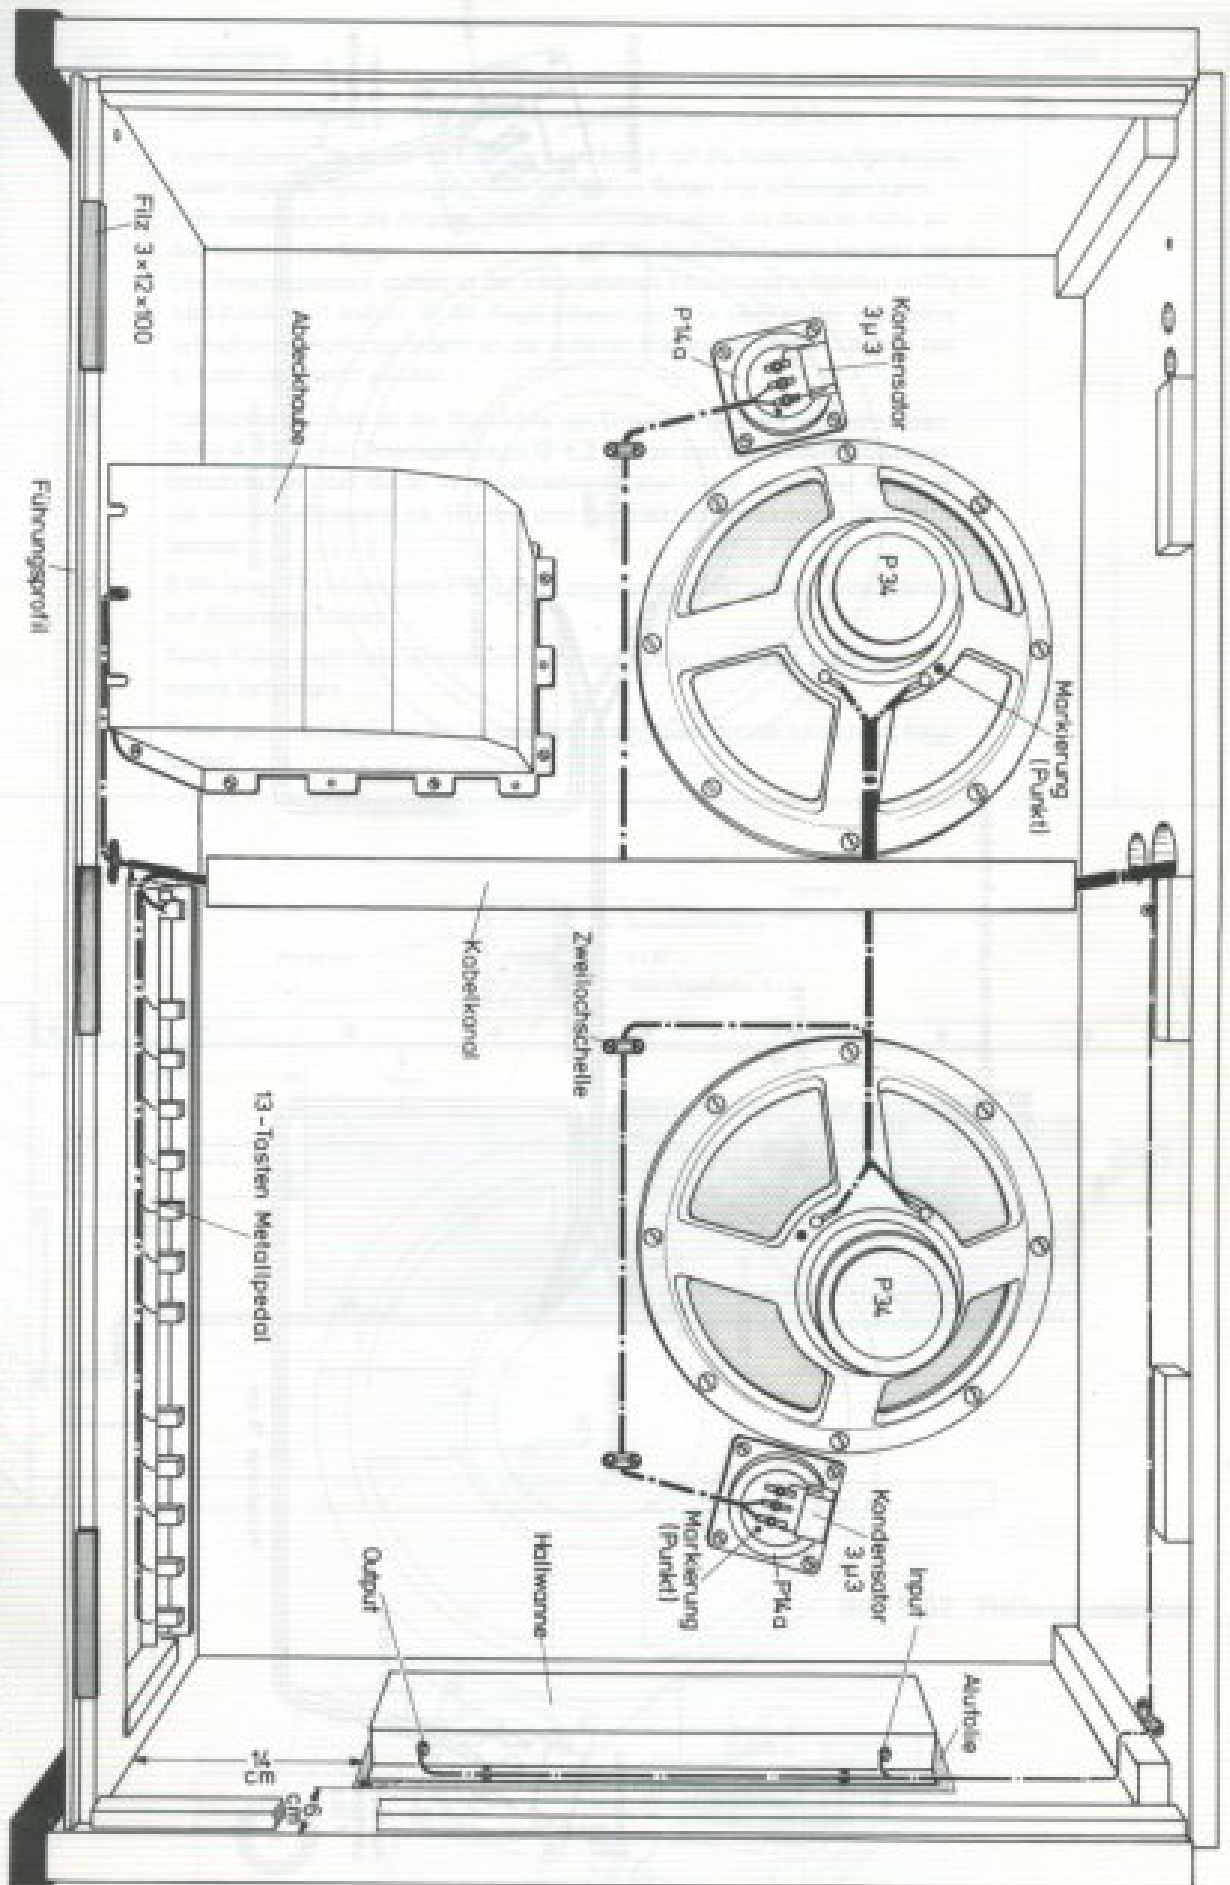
Lautsprecher- und Hallwärmeneinbau
